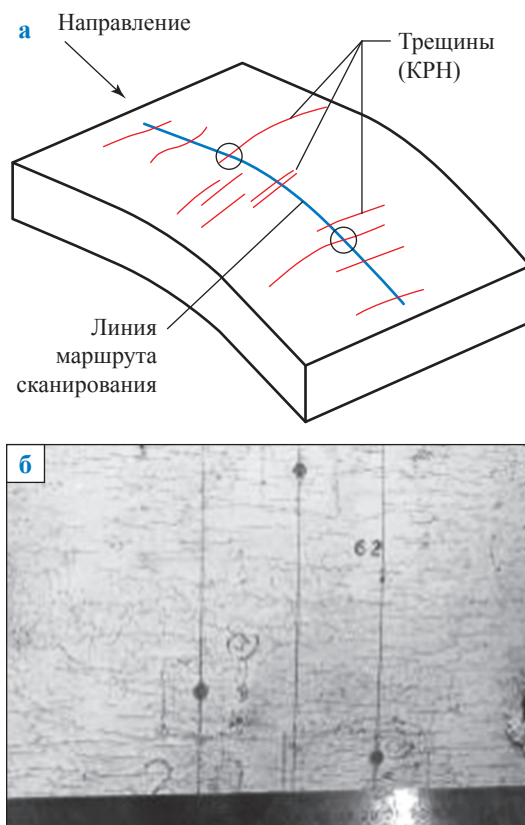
Схема (а) и пример (б) образца с размеченными маршрутами и контрольными точками для измерений
